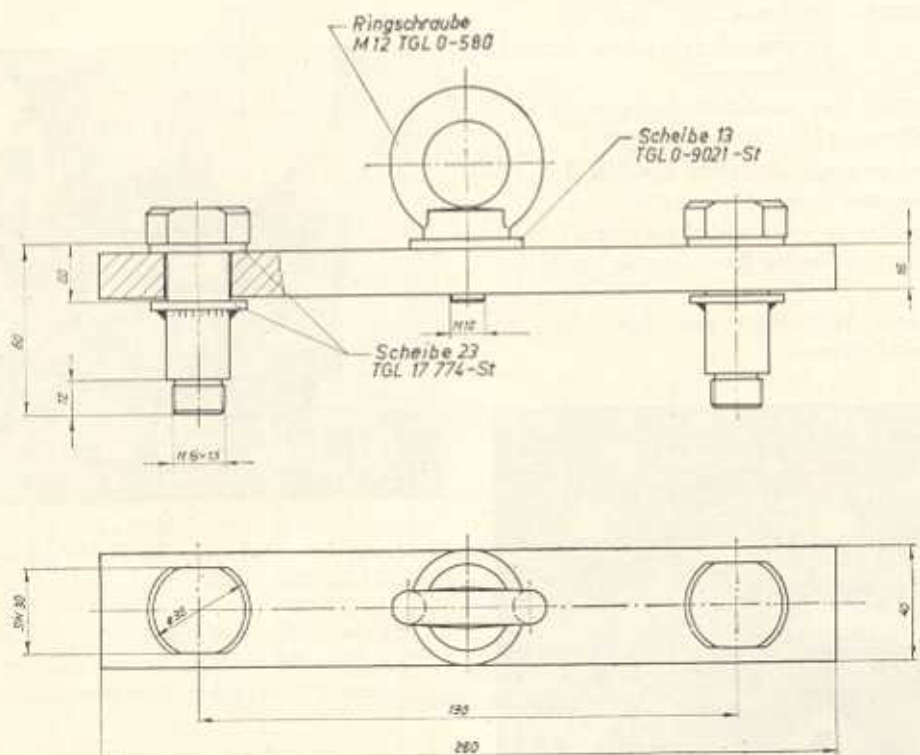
Aushebevorrichtung für Motor (Maßzeichnung)
